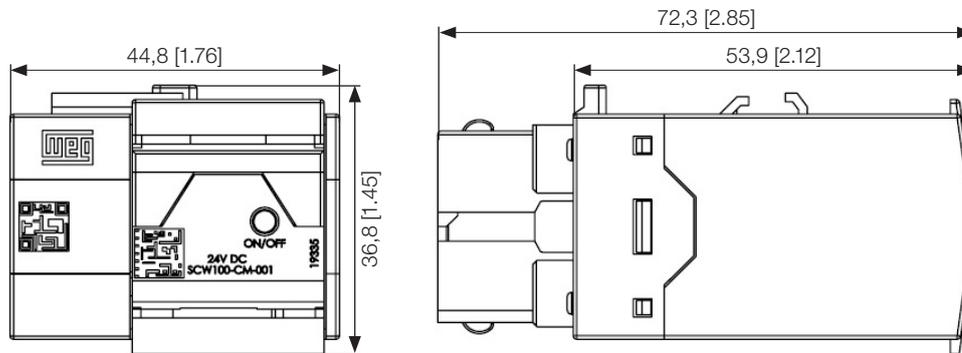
Dimensões do Módulo de Conexão Partida Direta (CM-001) em mm [in]
